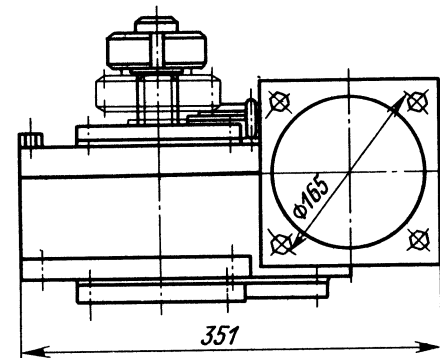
Механизм привода кисти руки с планетарным редуктором для ПР "Универсал-15"
